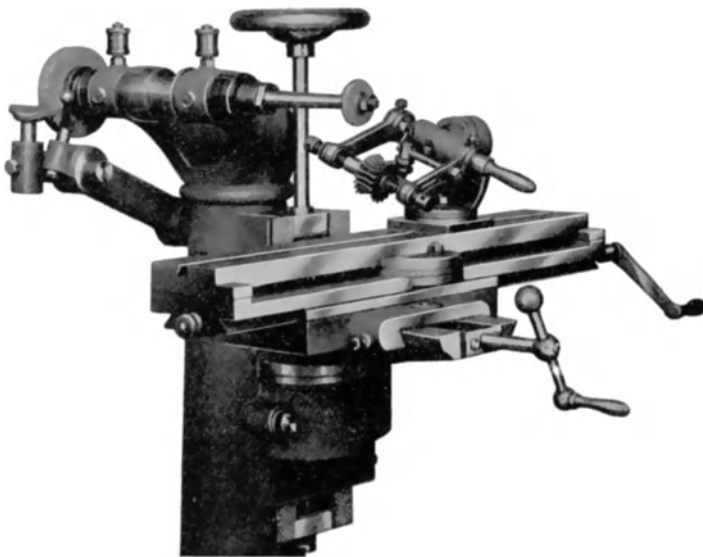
Das Schärfe eines gerieften Profilfräasers mit dem Drehteil des Universalböckchens.
